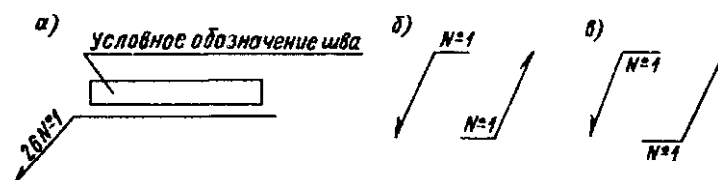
Нумерация одинаковых сварных швов
